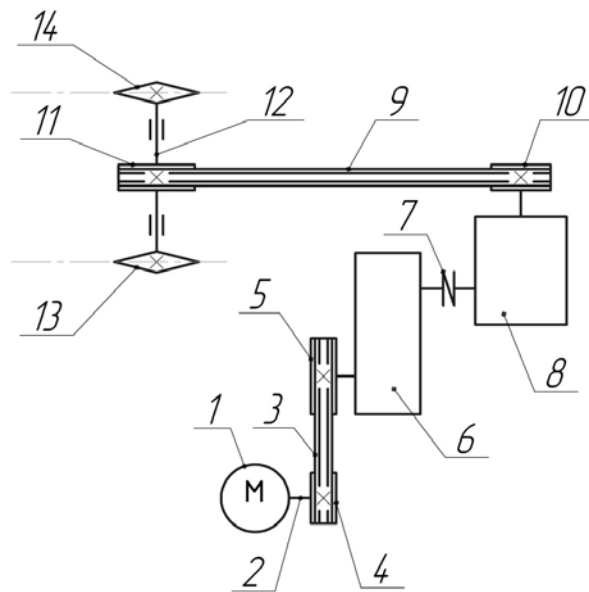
Кінематична схема привода рукавичного автомата з варіатором
